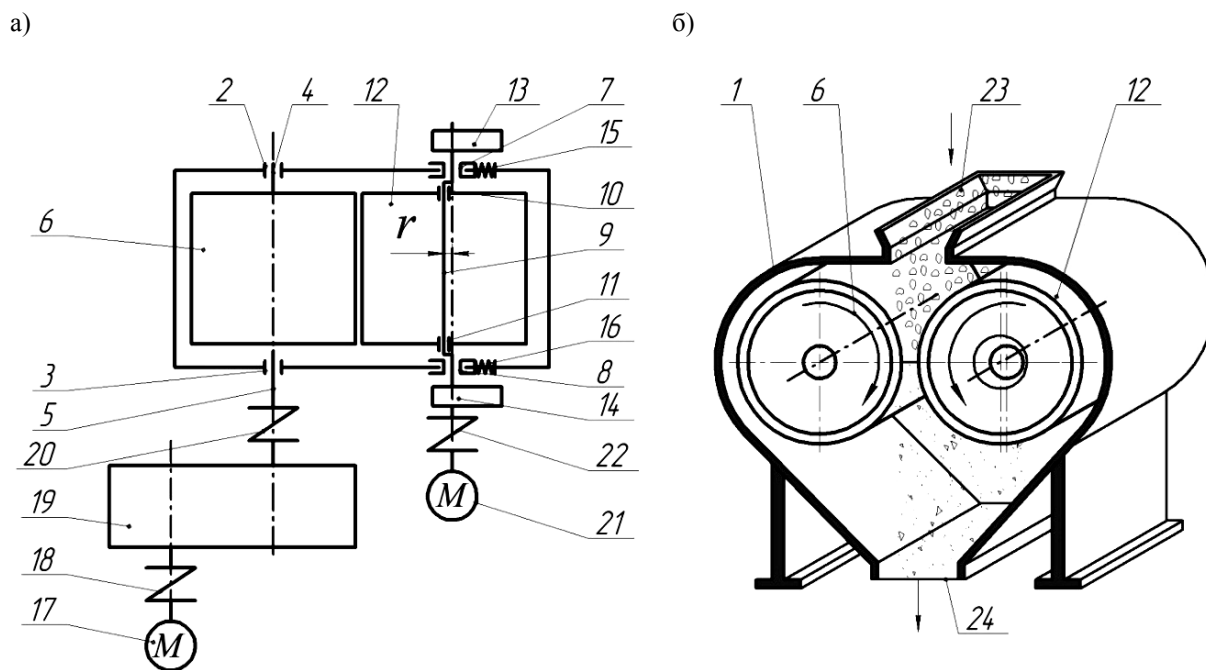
Схема вибровалкового измельчителя ВВИ1: а – вид сверху; б – вид сбоку
